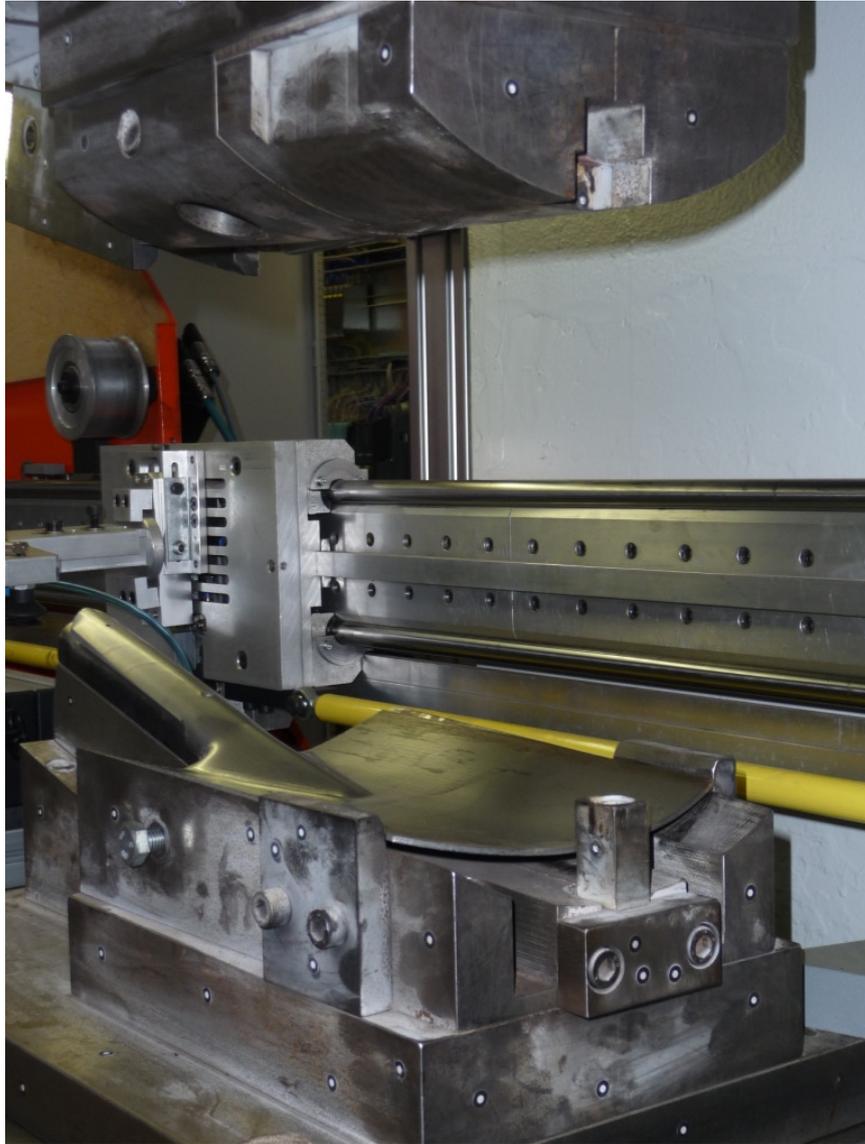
Umformpresse mit Werkzeug und umgeformter Platine (Aufnahmedatum 20.06.12)
